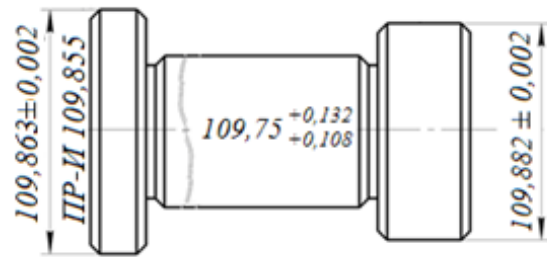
Эскиз калибра-пробки для контроля диаметров коренных опор двигателя ЯМЗ
